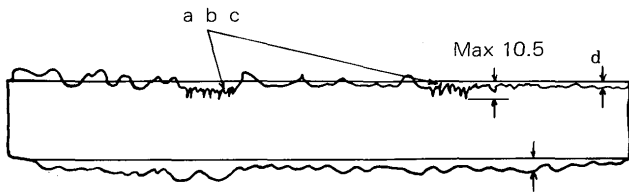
Schweißfläche: Eingußseite (b)
